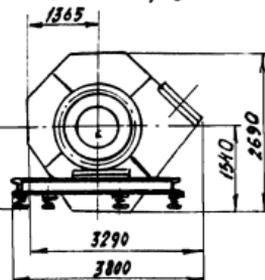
Вентилятор ВЦН-75-16-02 виброизолированный (исполнение б) левую вращения. Положения корпусов.
